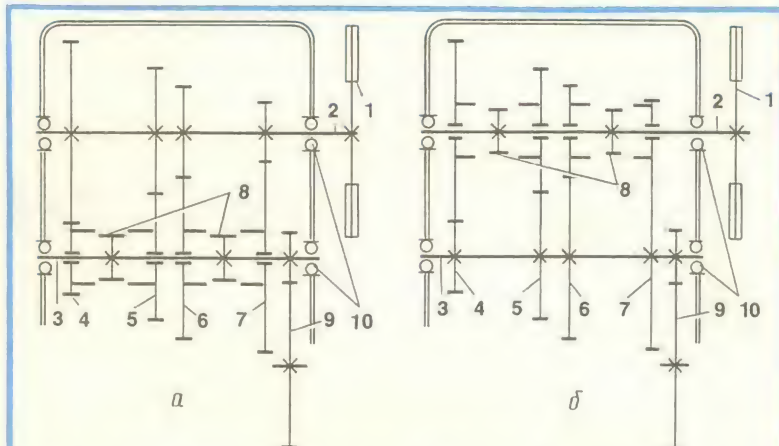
Варианты расположения шестерен в двухвальной коробке передач: а — зафиксированы зубчатые колеса на первичном валу; б — на вторичном валу; 1 — ведомый диск сцепления; 2 — первичный вал; 3 — вто-
